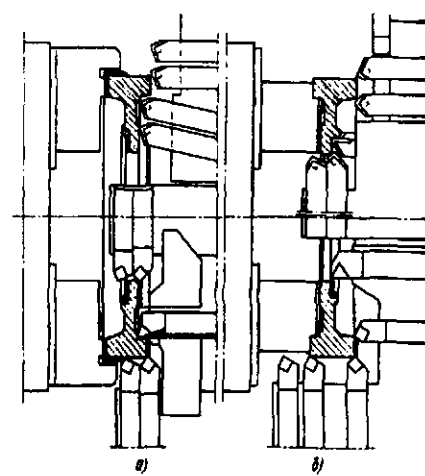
Наладка горизонтального двухшпиндельного фронтального полуавтомата для обработки заготовок зубчатых колес: а – обработка при первом установе; б – обработка при втором установе
